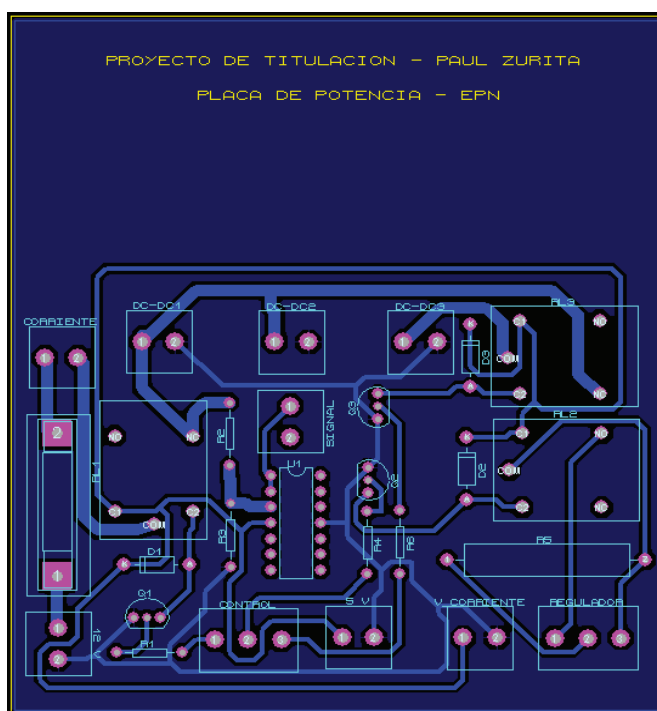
PCB en ARES de Proteus 7, placa de potencia.
